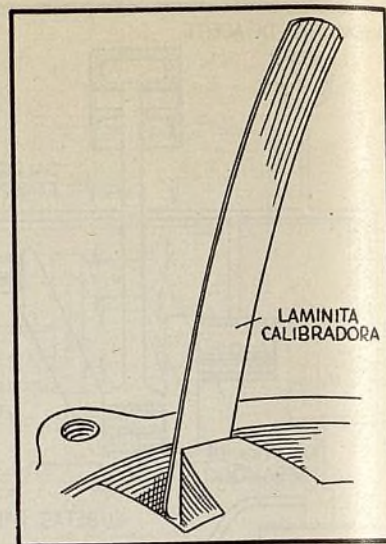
Verificación del intersticio entre el engranaje de la bomba de aceite y la caja de la bomba, mediante laminita calibradora. De ser este intersticio mayor de 0,004", el engranaje debe reemplazarse.
